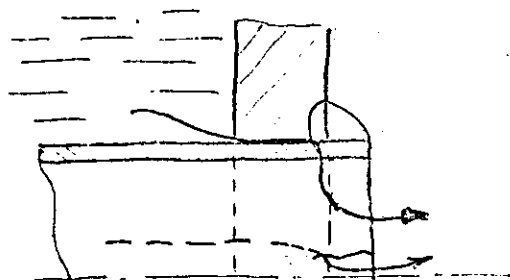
Fisuras que aparecen en el tubo y en la soldadura.
